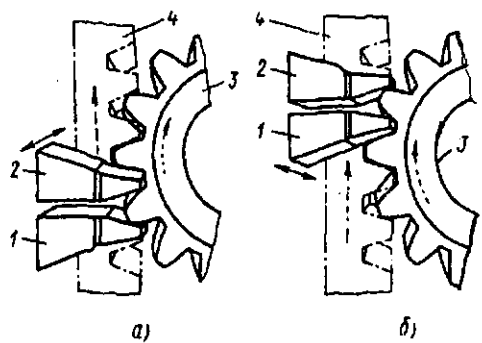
Схемы расположения зубострогальных резцов: а – в начале резания; б – в конце резания
